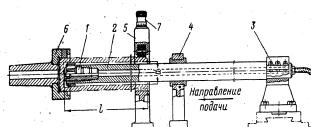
Схема наладки токарного станка для скоростного растачивания цилиндров.
